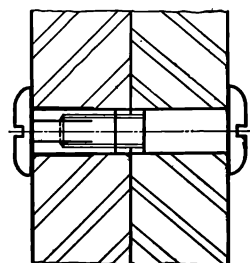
Схема соединения шкафов резьбовыми стяжками
